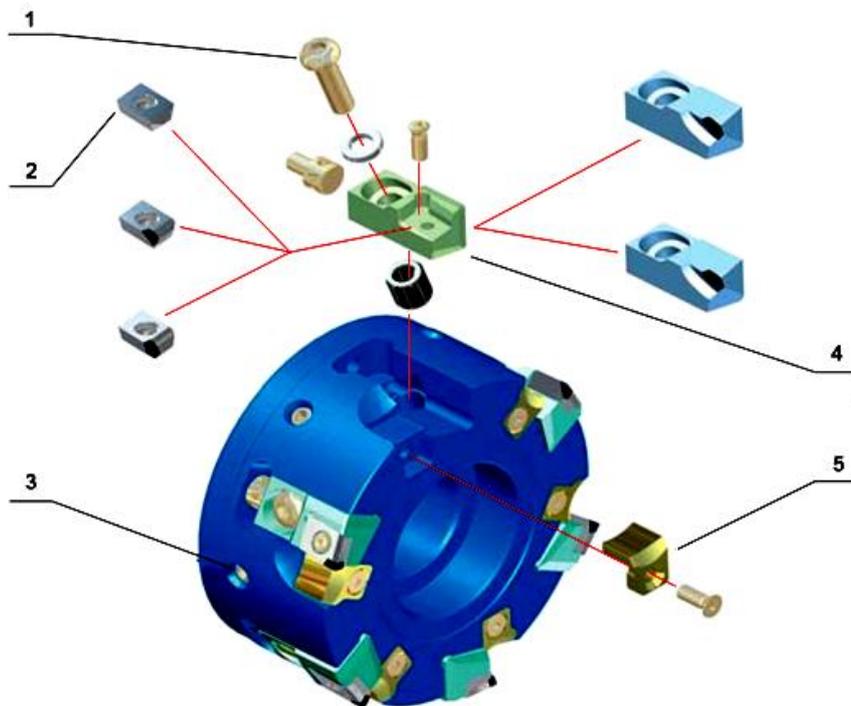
Крепление картриджей к корпусу фрезы фирмы «Sandvik Coromant»: 1 – винт крепежный; 2 – пластина режущая; 3 – винт балансирующий; 4 – картридж; 5 – пластина стружконаправляющая
